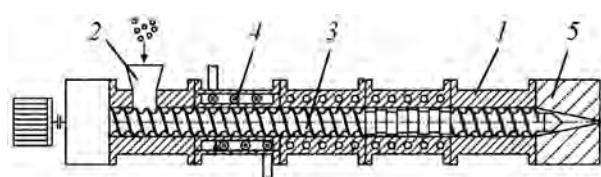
Черв'ячний екструдер [17]: 1 – корпус; 2 – завантажувальне вікно корпуса; 3 – черв'як; 4 – котушка індуктивності; 5 – екструзійна головка.
